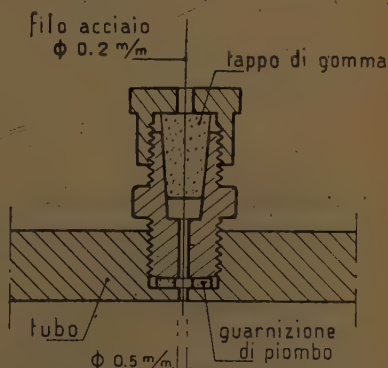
Particolare dell'attraversamento del cavetto d'acciaio.
